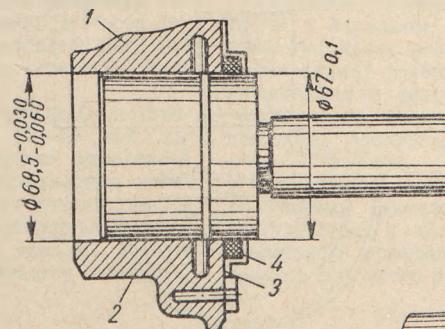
Опрессовка заднего сальника коленчатого вала:
